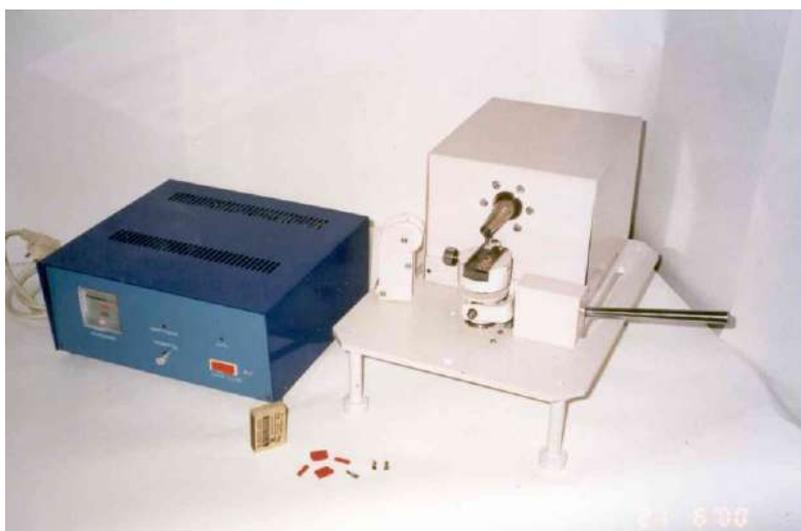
Внешний вид ультразвуковой сварочной машины типа УЗСМ1-0,1/22
